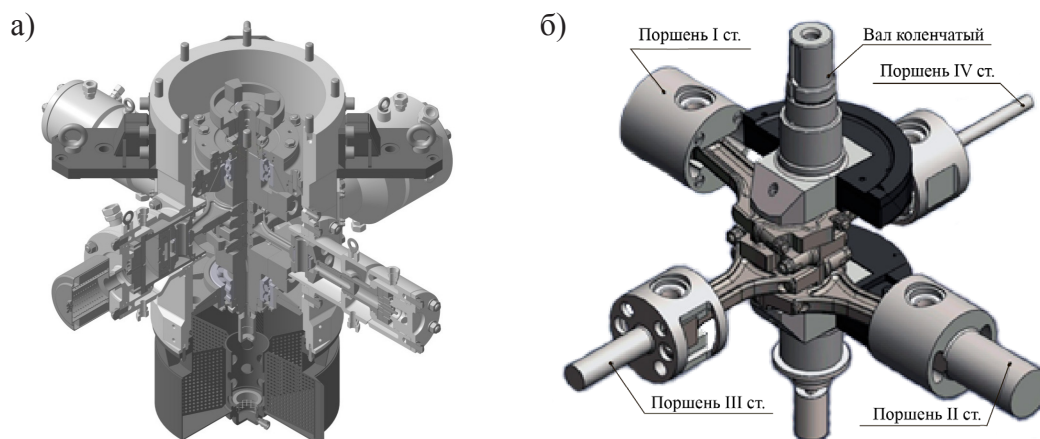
Схема компрессора с вертикальным валом: а) общий вид; б) механизм движения
